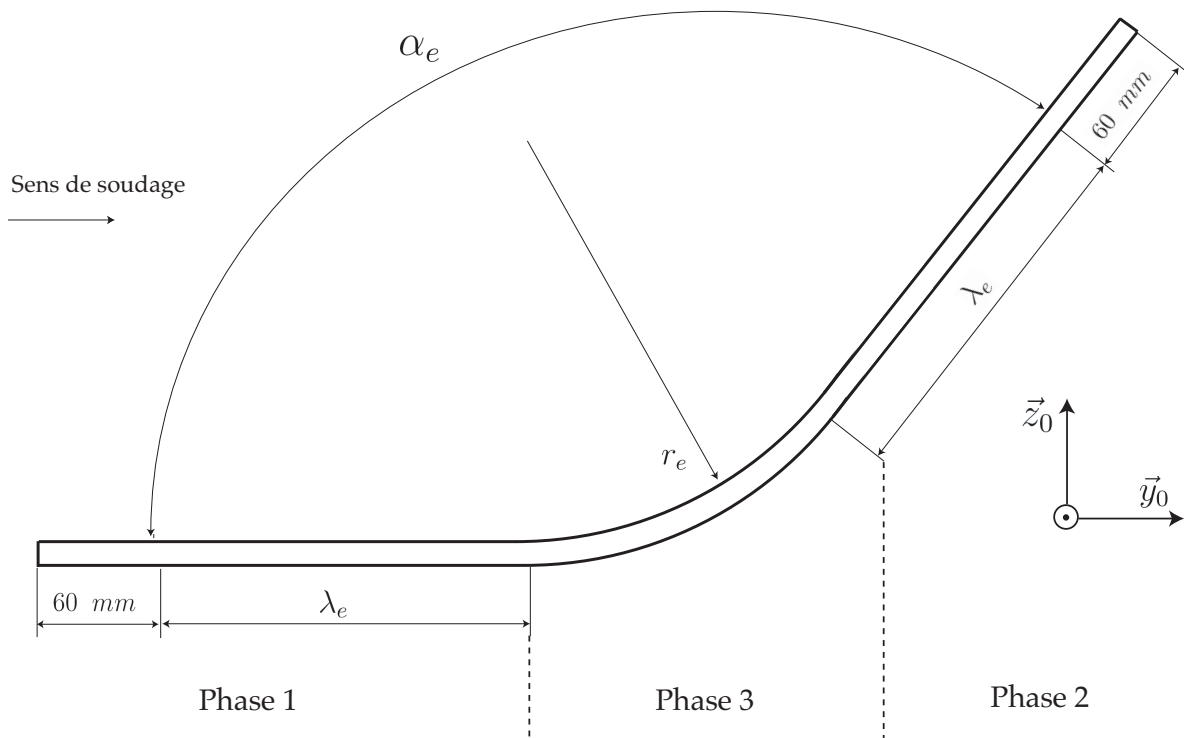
Définition du profil du cordon de soudure étudié.
